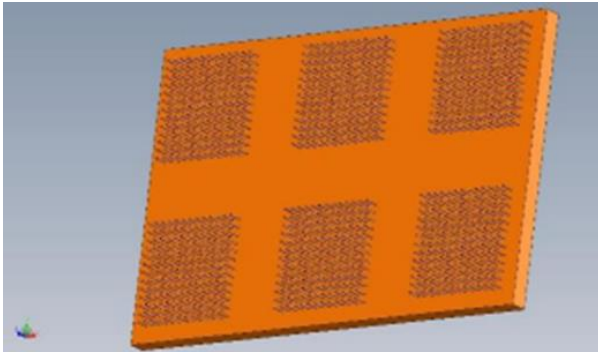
Nadelarray aus Kupfer, passend zur PCB-Platine
